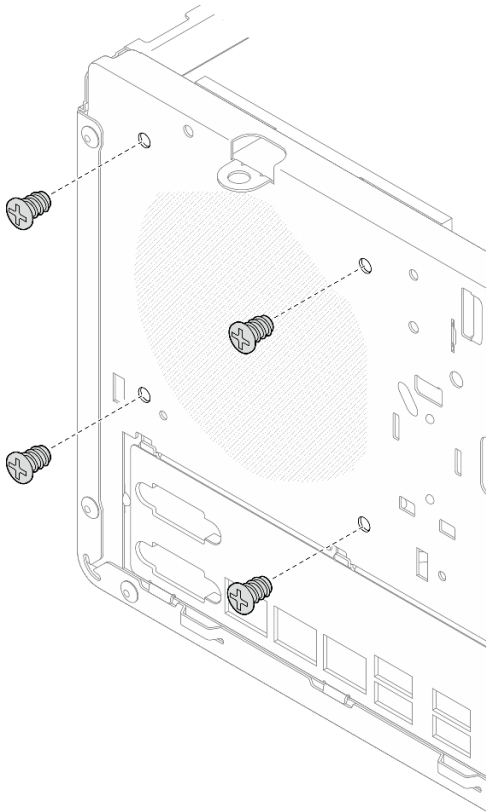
Entfernen der vier Schrauben, mit denen der Kühlkörper-Lüfter am Gehäuse befestigt ist
